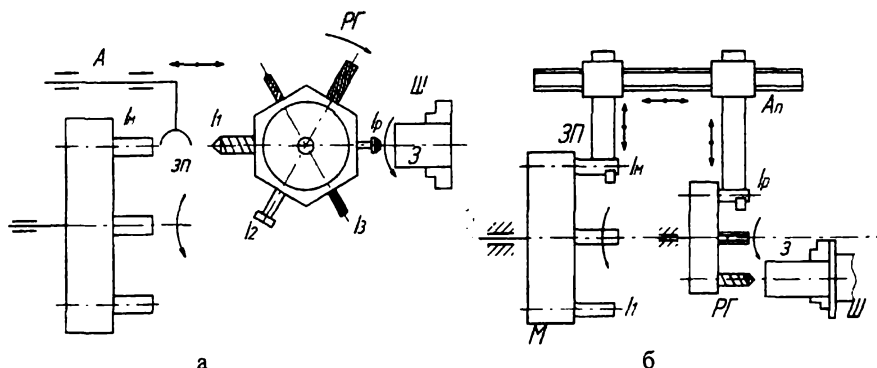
Спосіб заміни інструментів за допомогою магазину, автооператора та револьверної головки:
